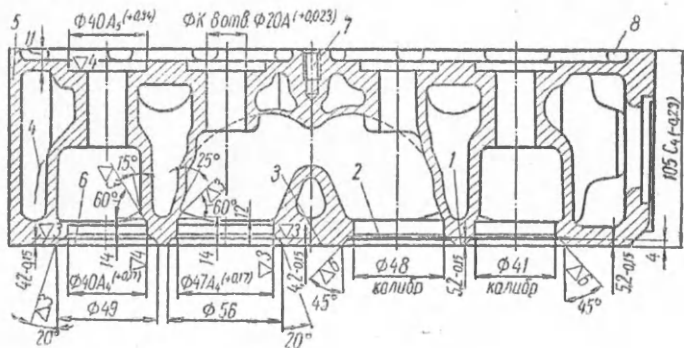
Головка блока цилиндров двигателя СМД-14 (разрез по клапанным гнездам).
